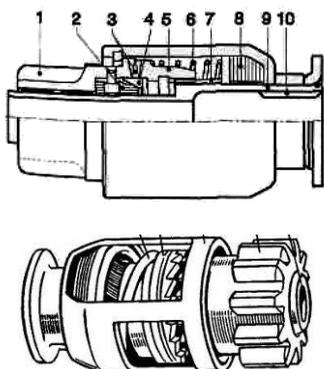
Обгінна муфта з храповим механізмом: 1 - шестерня стартера; 2 - сухар; 3 - радіальні зуби; 4 - роз'єднуюче кільце; 5 - гайка напівмуфти; 6 - пружина; 7 - спіральні шліци; 8 - гумовий буфер; 9 - втулка; 10 - шліци
